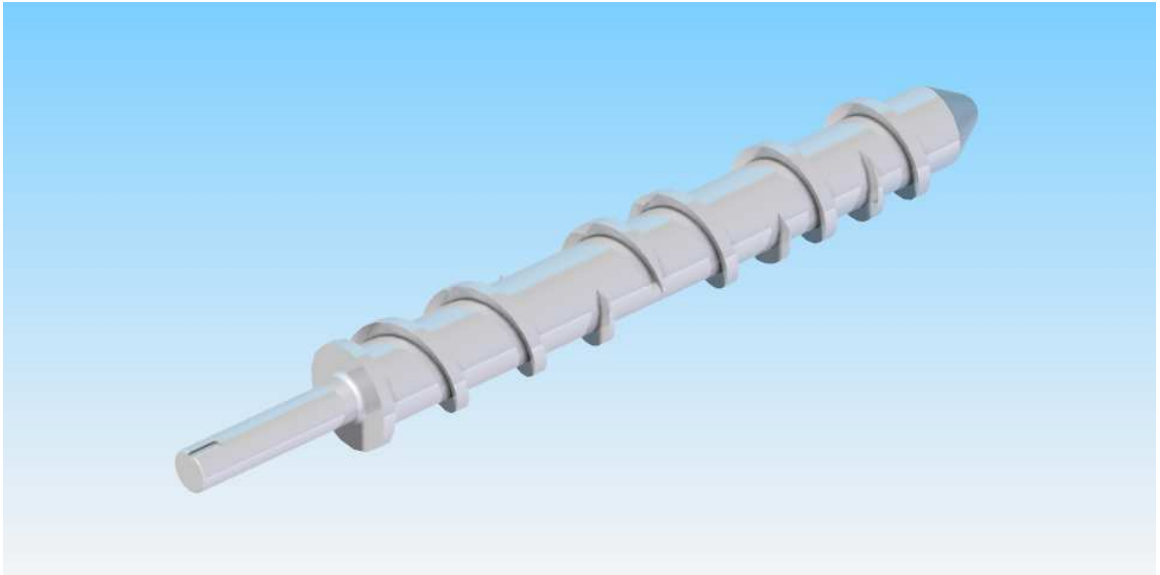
, Tornillo de extrusión en vista isométrica, fuente, López William.
